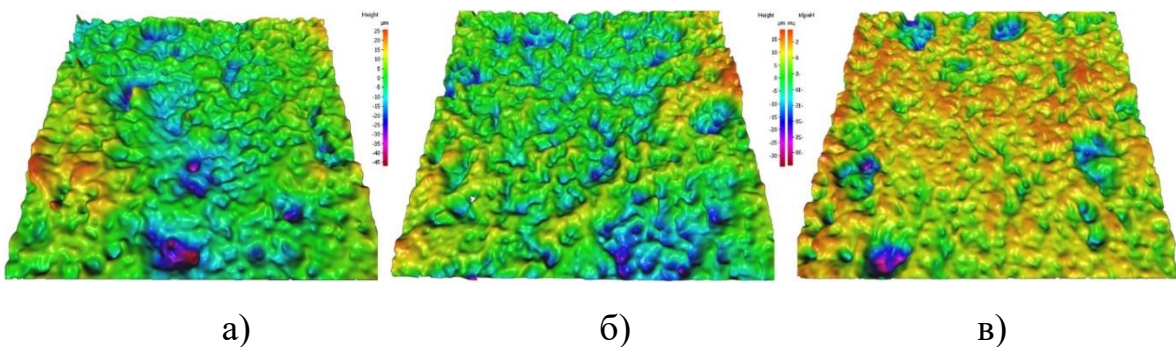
Морфологія поверхні після електроерозійного фрезерування [22]:
